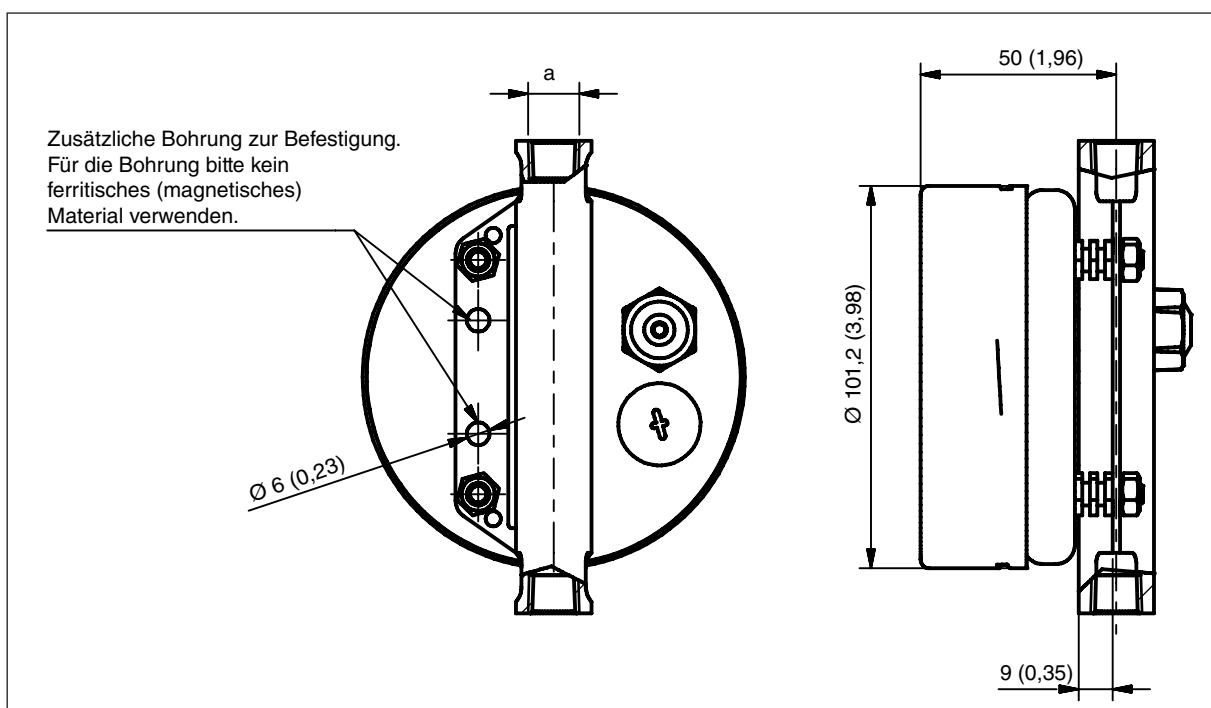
Rückansicht mit Befestigungsbohrungen, Abmessungen in mm (Zoll)
